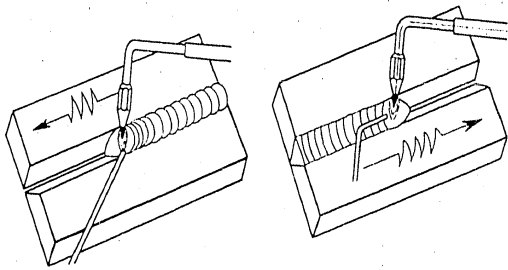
Nachlinksschweißung Bild 156: Nachrechtsschweißung
